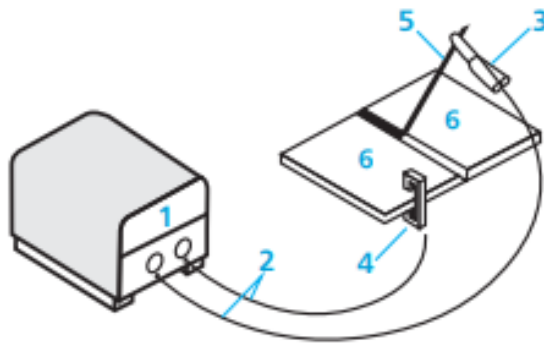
Elementos del Circuito de Soldadura por Arco Eléctrico
